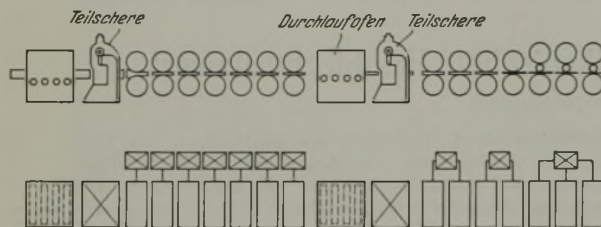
Schema einer kontinuierlichen Feinblech- und Sturzenstraße.
